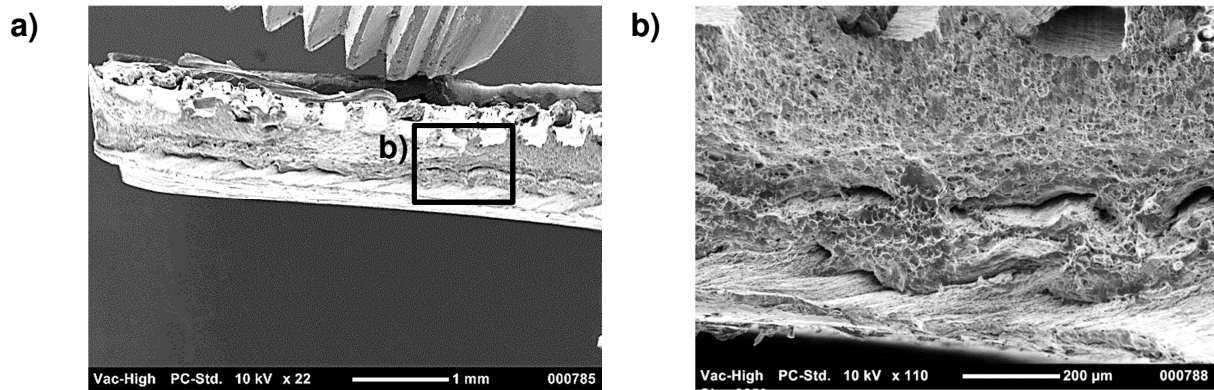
Fraktographische Detailaufnahmen der FSW-Verbindung IMWF-33-00033
